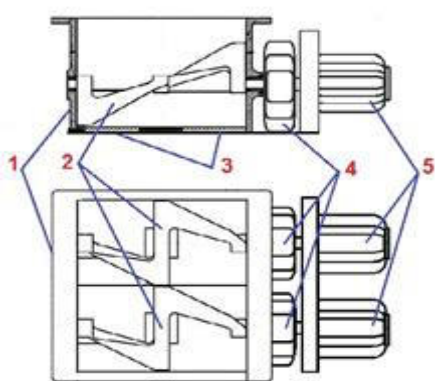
Схема установки карбоксиметилирования крахмала в твердой фазе. 1-бункер, 2-Z-образные лопасти, 3-ниши для отгрузки продукта, 4-редукторы, 5-электродвигатели
